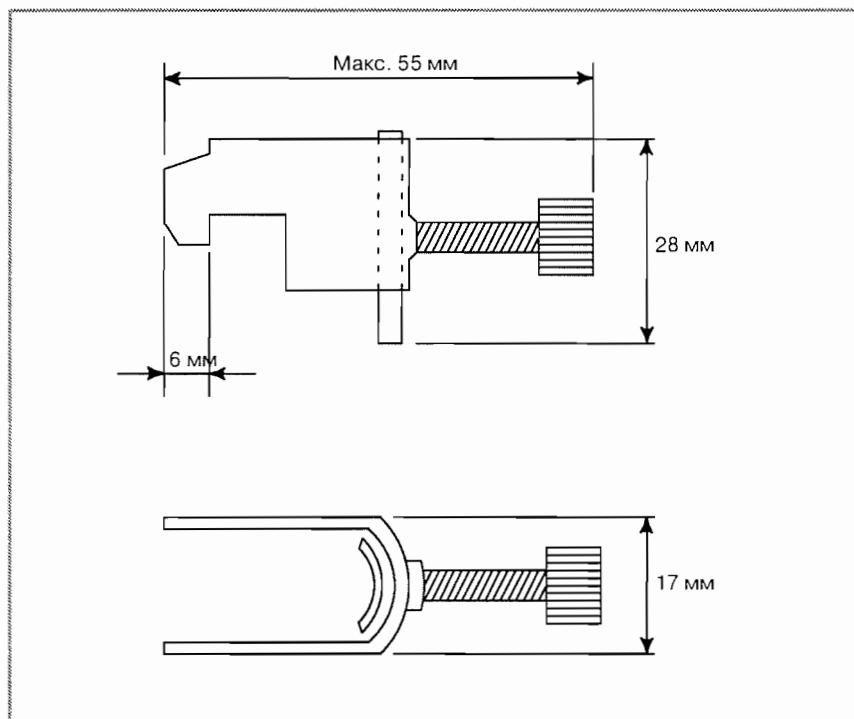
(е) Габаритные чертежи металлической арматуры для крепления
